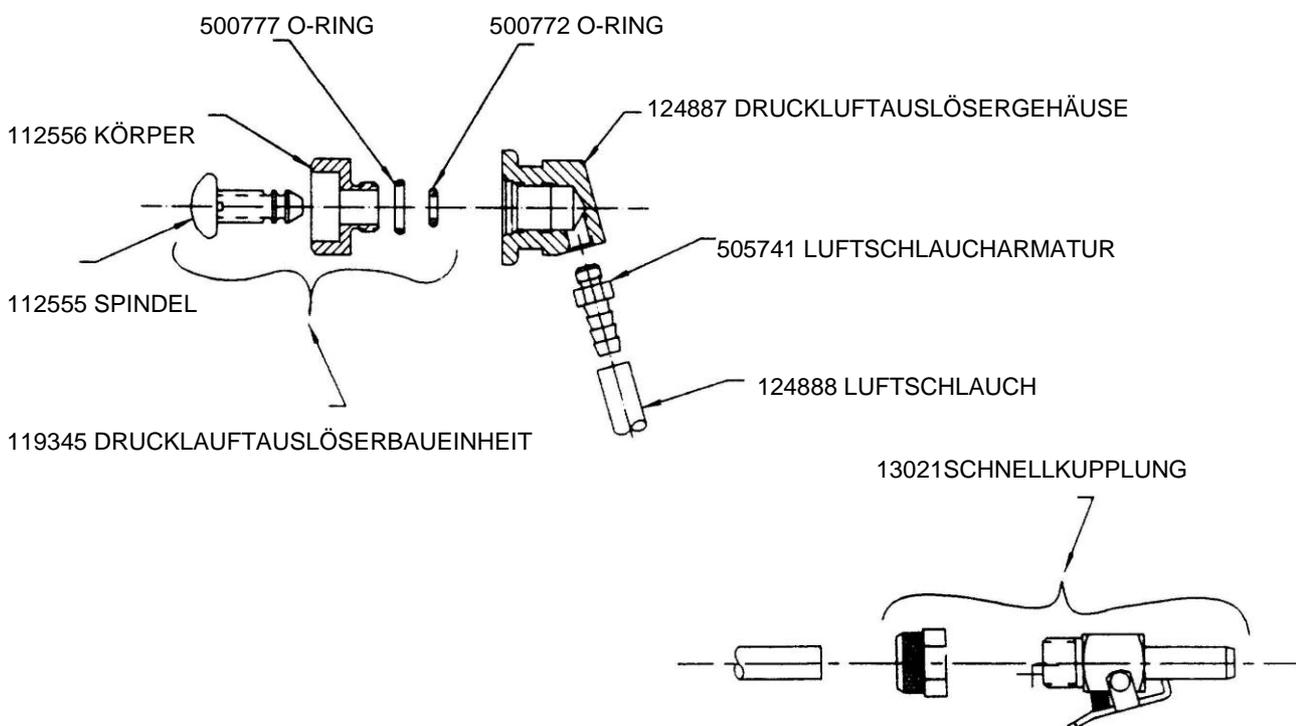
A – Explosionszeichnung – Druckluftauslöser und Schnellkupplung
